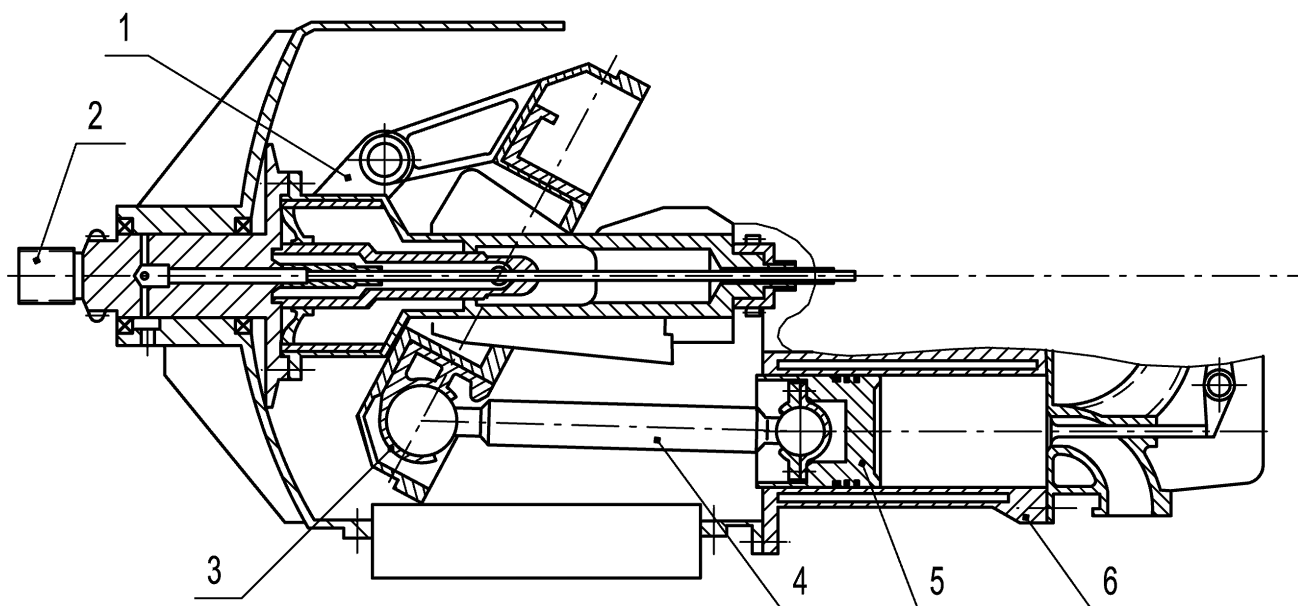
Аксиальный двигатель с переменным ходом поршня конструкции Н. Welsh и С. Riley:
